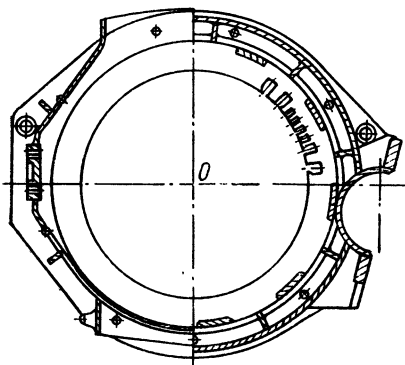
Сварная станина двигателя однофазного тока
